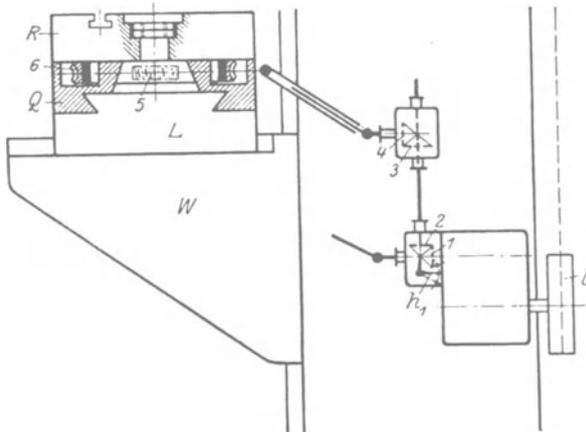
Rundsteuerung für den Drehtisch *R*.
